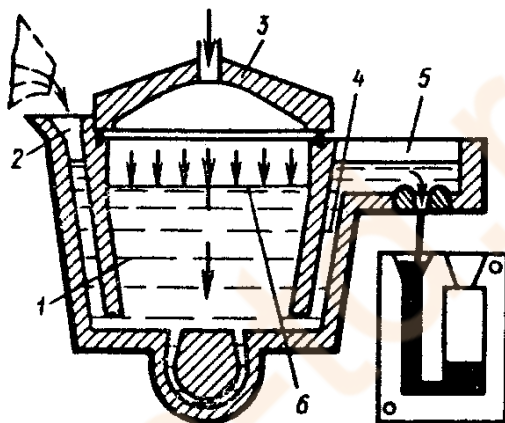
Пневматический дозатор для заливки чугуна в процессе выдачи дозы: 1 – ванна канальной индукционной печи; 2 – заливочный металлопровод; 3 – крышка; 4 – выпускной металлопровод; 5 – сливная камера; 6 – зеркало расплава чугуна
